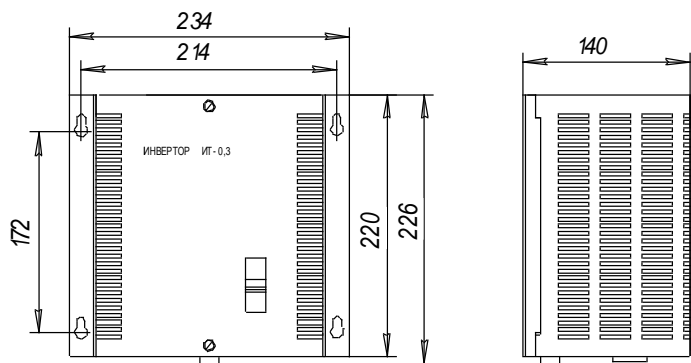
Габаритный чертеж инвертора ИТ-0,3
